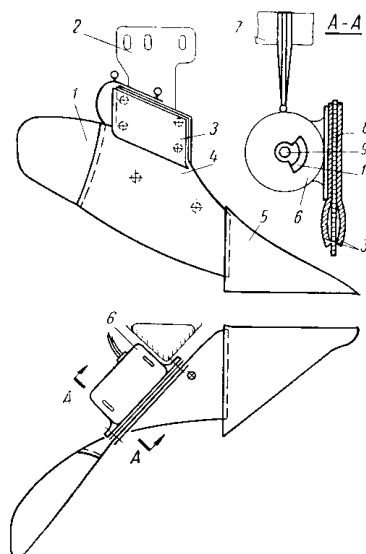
Корпус плуга з пристроєм, що запобігає залипання лемешно-полицевої поверхні.
